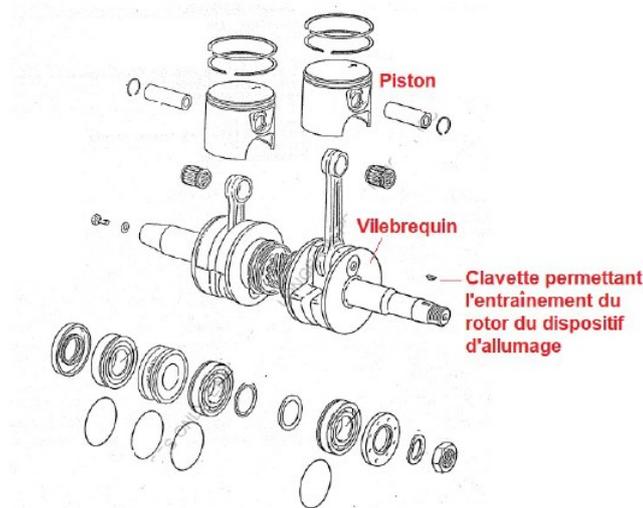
sous-ensemble du bloc moteur Rotax 535C (Source : Rotax)
